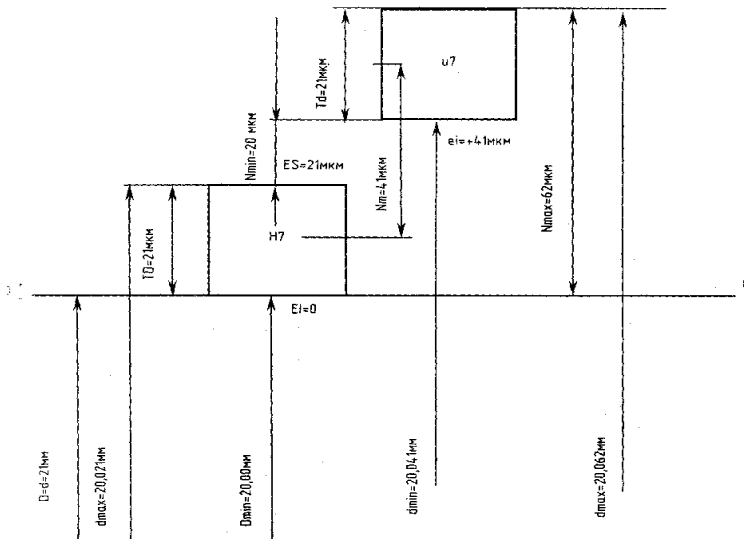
Схема розташування полів допусків посадки з натягом деталей з'єднання.
